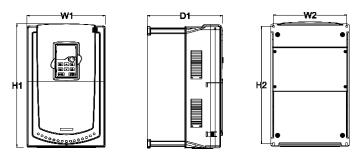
Настенный монтаж 1.5 – 30 кВт
